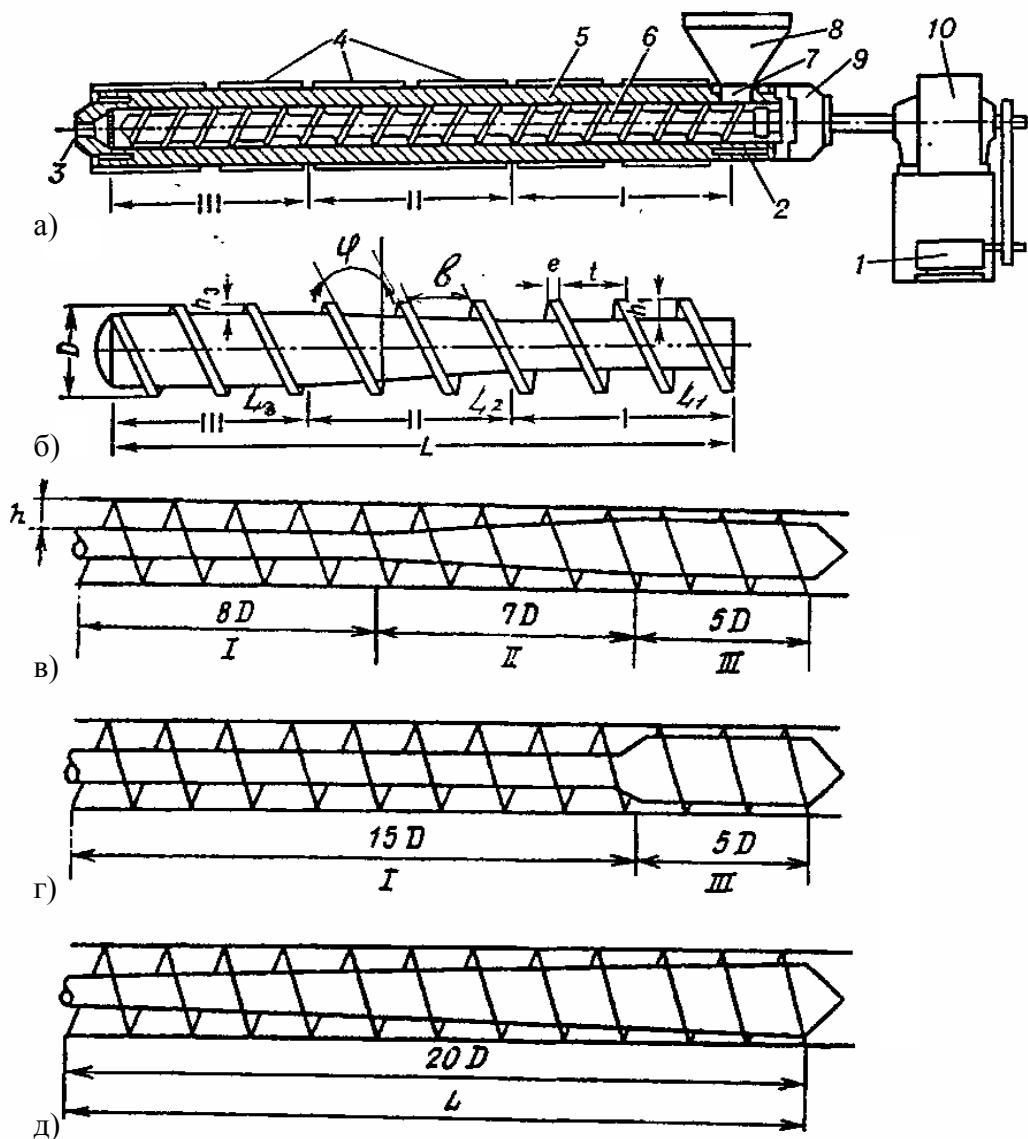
Одночервячный горизонтальный одностадийный экструдер (а) и червяк (б, в, г, д): 1 – двигатель, 2 – канал для охлаждения зоны бункера, 3 – канал для выхода расплава в профилирующую головку, 4 – нагреватели цилиндра (корпуса), 5 – цилиндр, 6 – червяк, 7 – загрузочная воронка, 8 – бункер, 9 – упорный подшипник, 10 – редуктор. Зоны червяка: I – питания (загрузки), II – сжатия (пластикации), III – выдавливания (дозирования). L – длина червяка; h_1, h_2, h_3 – глубина винтового канала в зонах питания, сжатия и пластикации соответственно; e – ширина гребня витка; t – шаг нарезки; v – ширина канала нарезки; D – диаметр шнека; φ – угол подъема винтовой линии шнека
